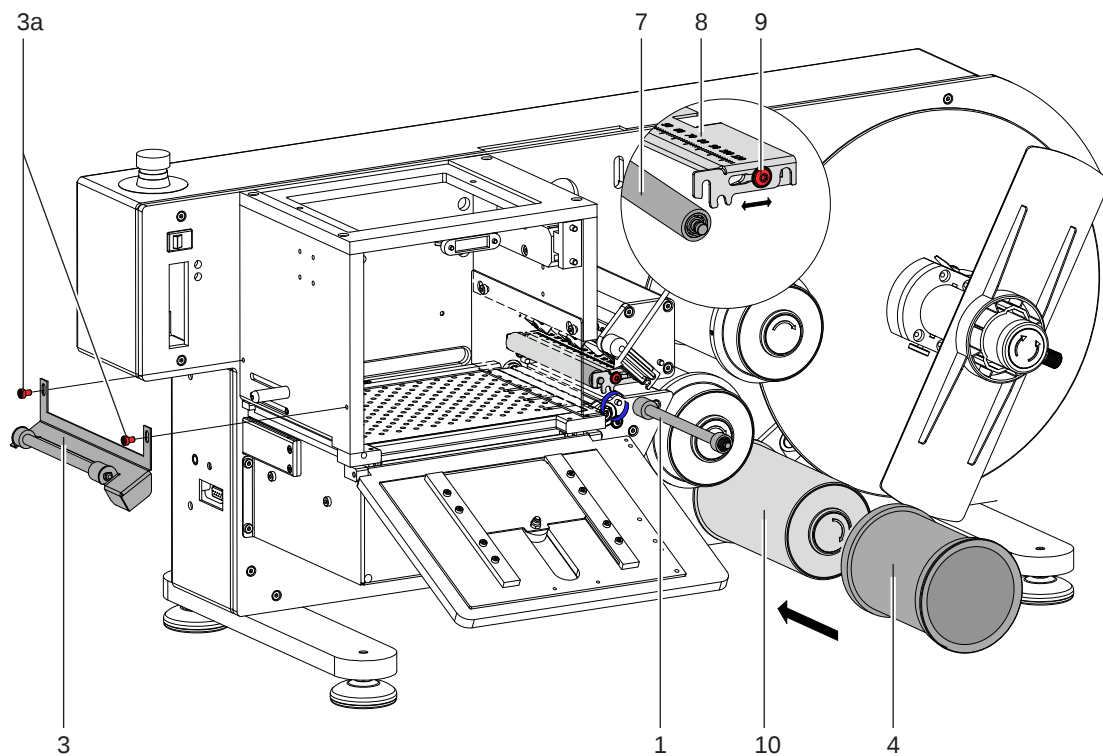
Wechsel /Anbau von Roller Tag - Komponenten
